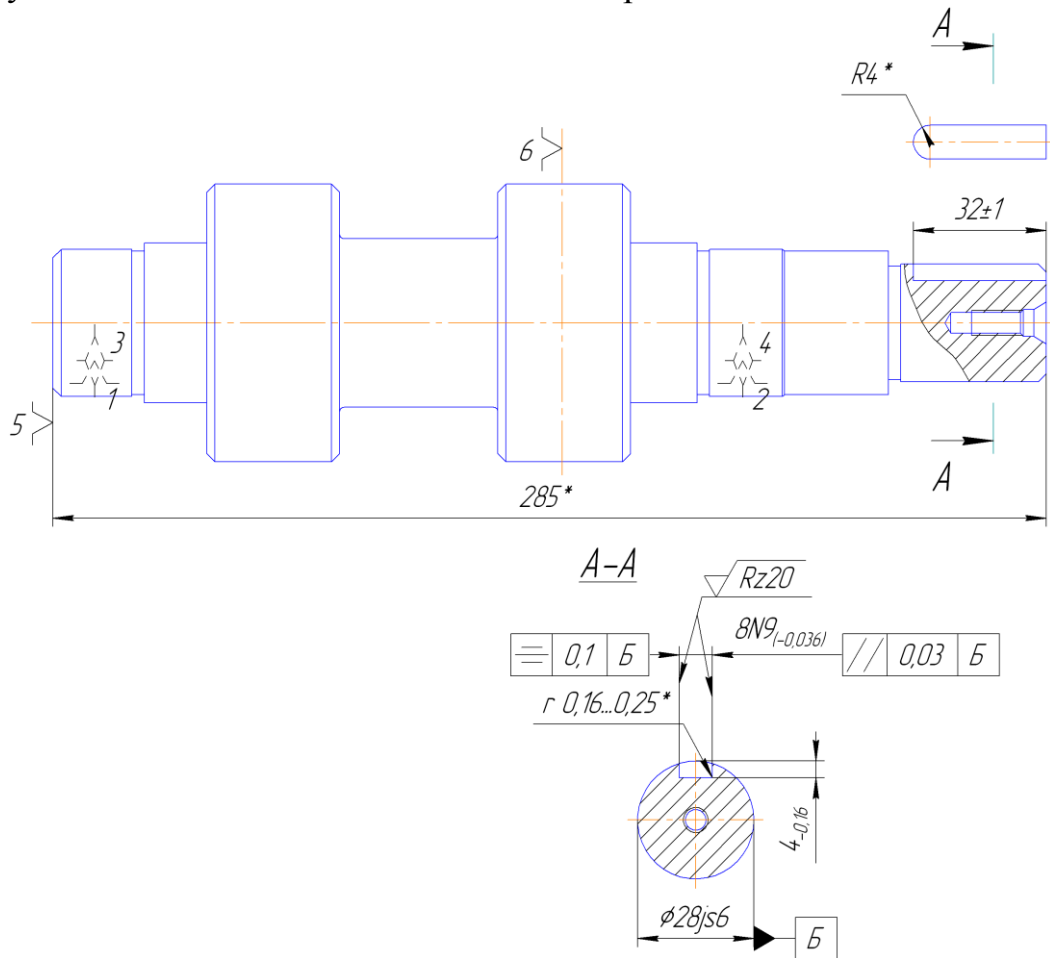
Ескіз на фрезерування паза 8N9<sub>(-0,036)</sub> вал-шестерні
